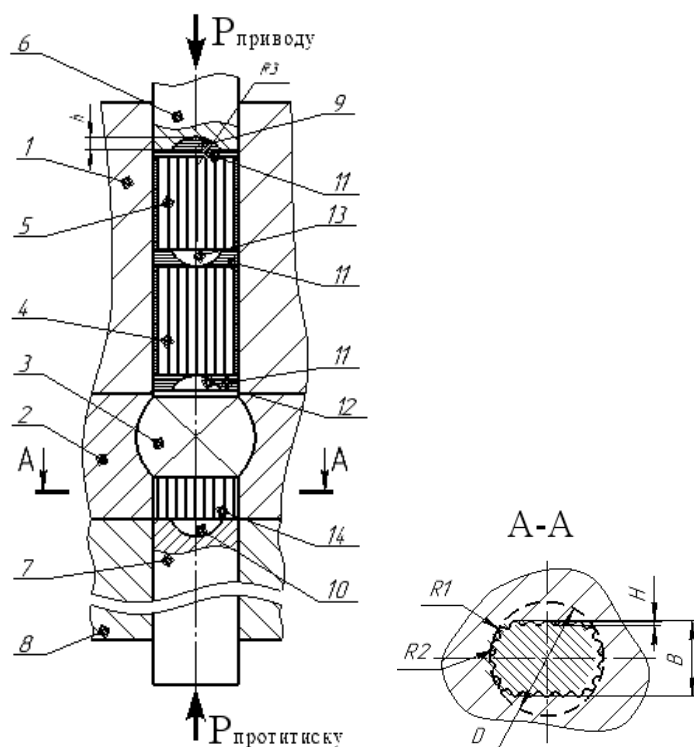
Схема пристрою для реалізації багатоетапного пресування заготовок пластичним середовищем
